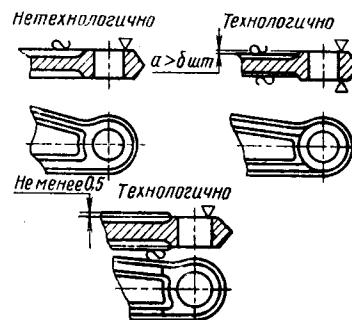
Выбор оптимального расположения обрабатываемых поверхностей к необрабатываемым в рычагах.
